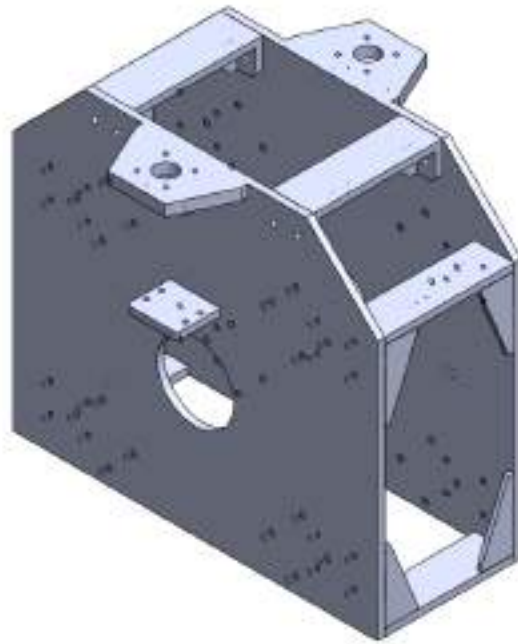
Vista isométrica del carro Z sin componentes ni accesorios.
